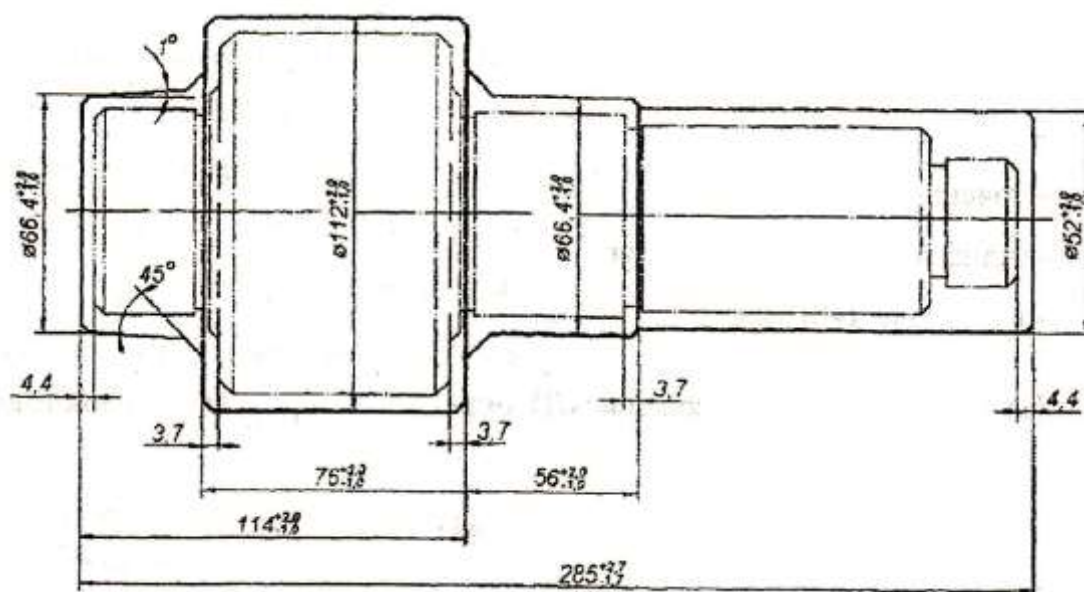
Заготовка шестерни ведущей (Рисунок 3) с начисленными припусками
